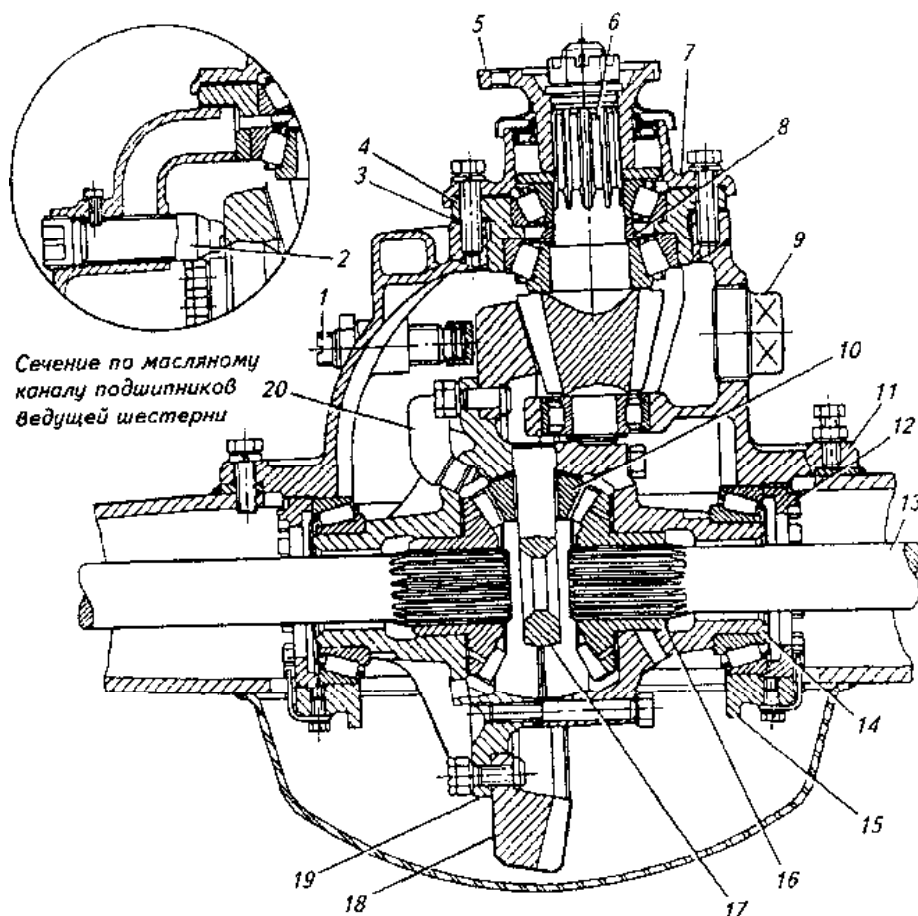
Одинарная главная передача автомобиля ГАЗ-53-12: 1 -упор- 2-маслоприемная трубка; 3- регулировочные прокладки; 4 - муфта подшипников; 5 –фланец; 6 -ведущая шестерня; 7, 15-крышки; 8-регулирующее кольцо, 9-пробка заливного отверстия; 10 - сателлит; 11 - картер; 12 - гайка; 13 - полуось; 14 - правая чашка коробки дифференциала; 16 - полуосевая шестерня; 17 - крестовина; 18 – ведомая шестерня; 19-левая чашка коробки дифференциала; 20- маслоулавливатель
